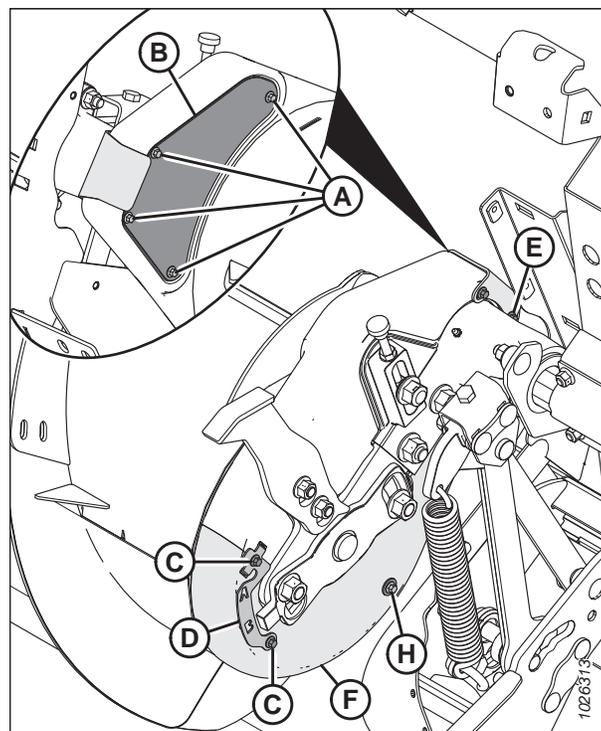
Entraînement de la vis d'alimentation – vue arrière
